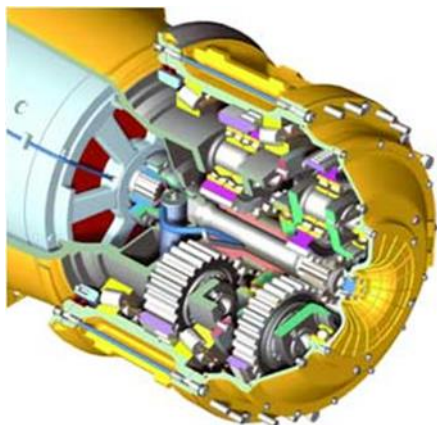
Редуктор мотор-колеса (PMK) самосвала
